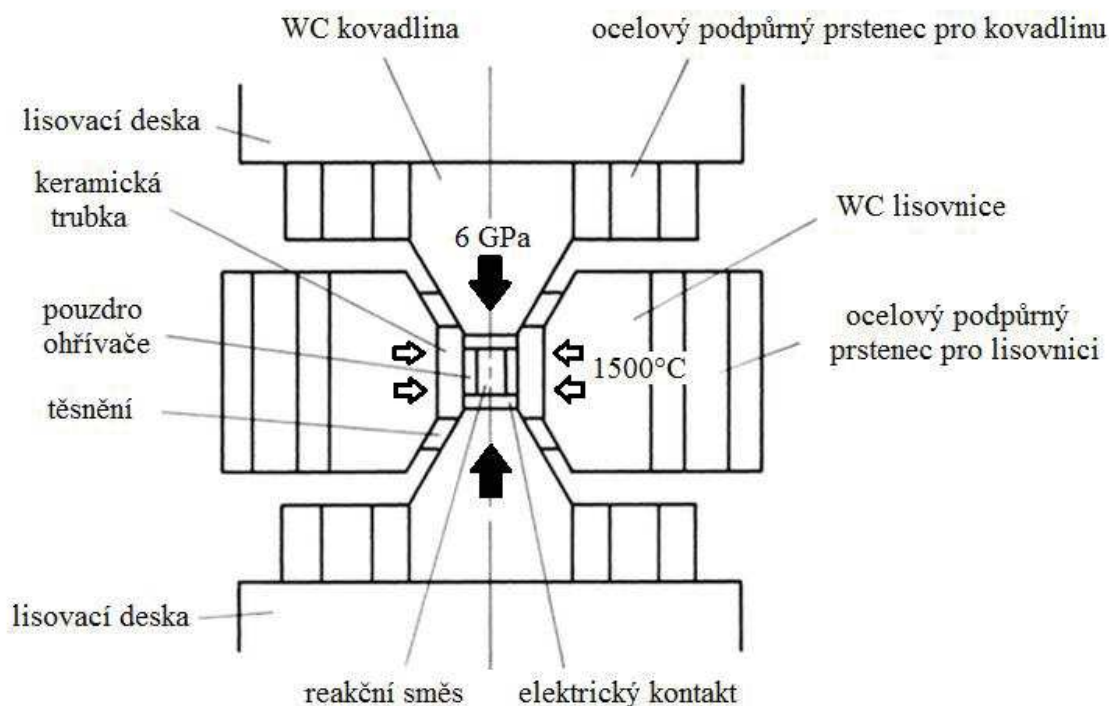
Dnešní moderní aparatura ve firmě Element Six [5].
